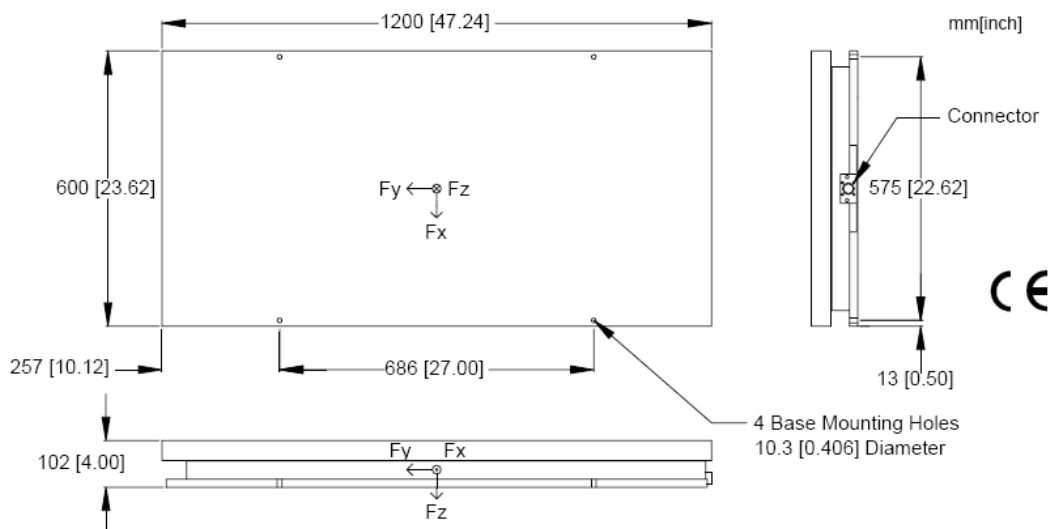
Dimensiones de la placa dinamométrica utilizada
